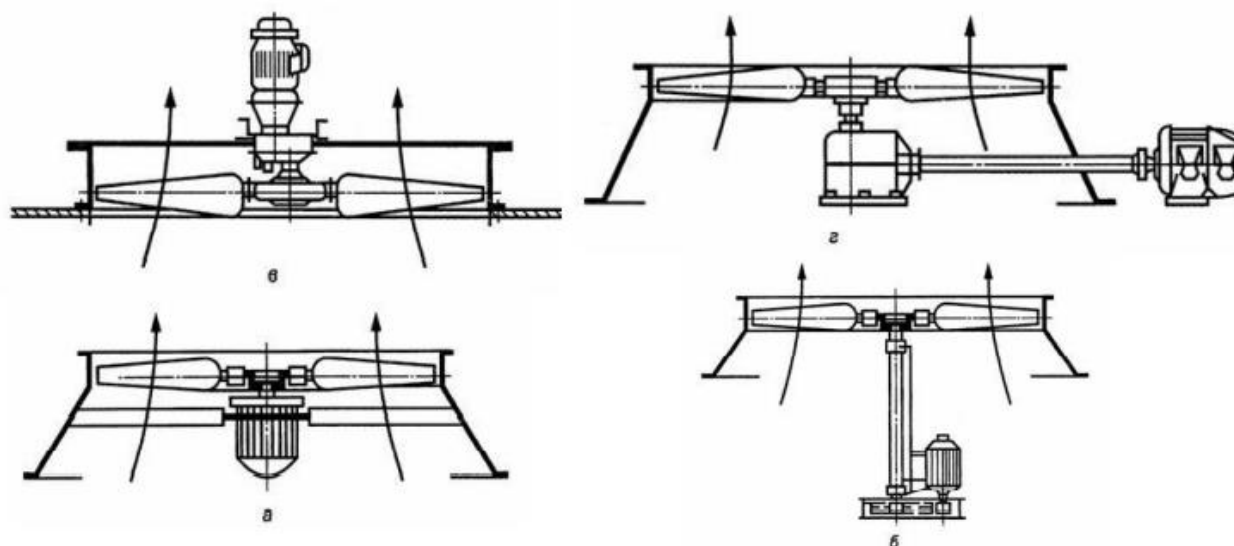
приводы аппаратов вытяжного вида: а - непосредственный; б - клиноременный; в - редуктор с параллельными валами; г - редуктор с перпендикулярными валами
